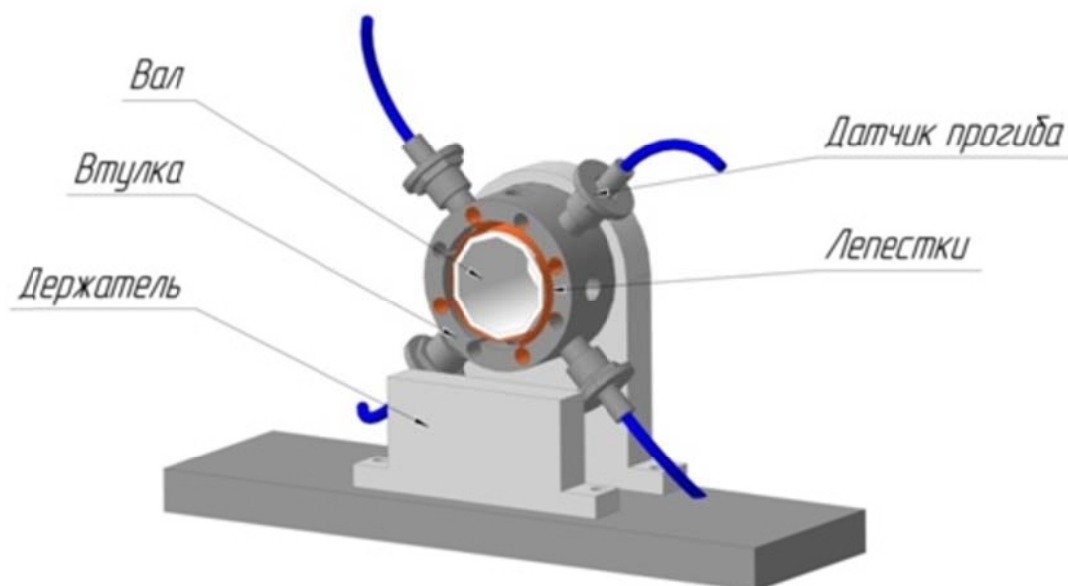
Подшипниковый узел с лепестковым газодинамическим подшипником
